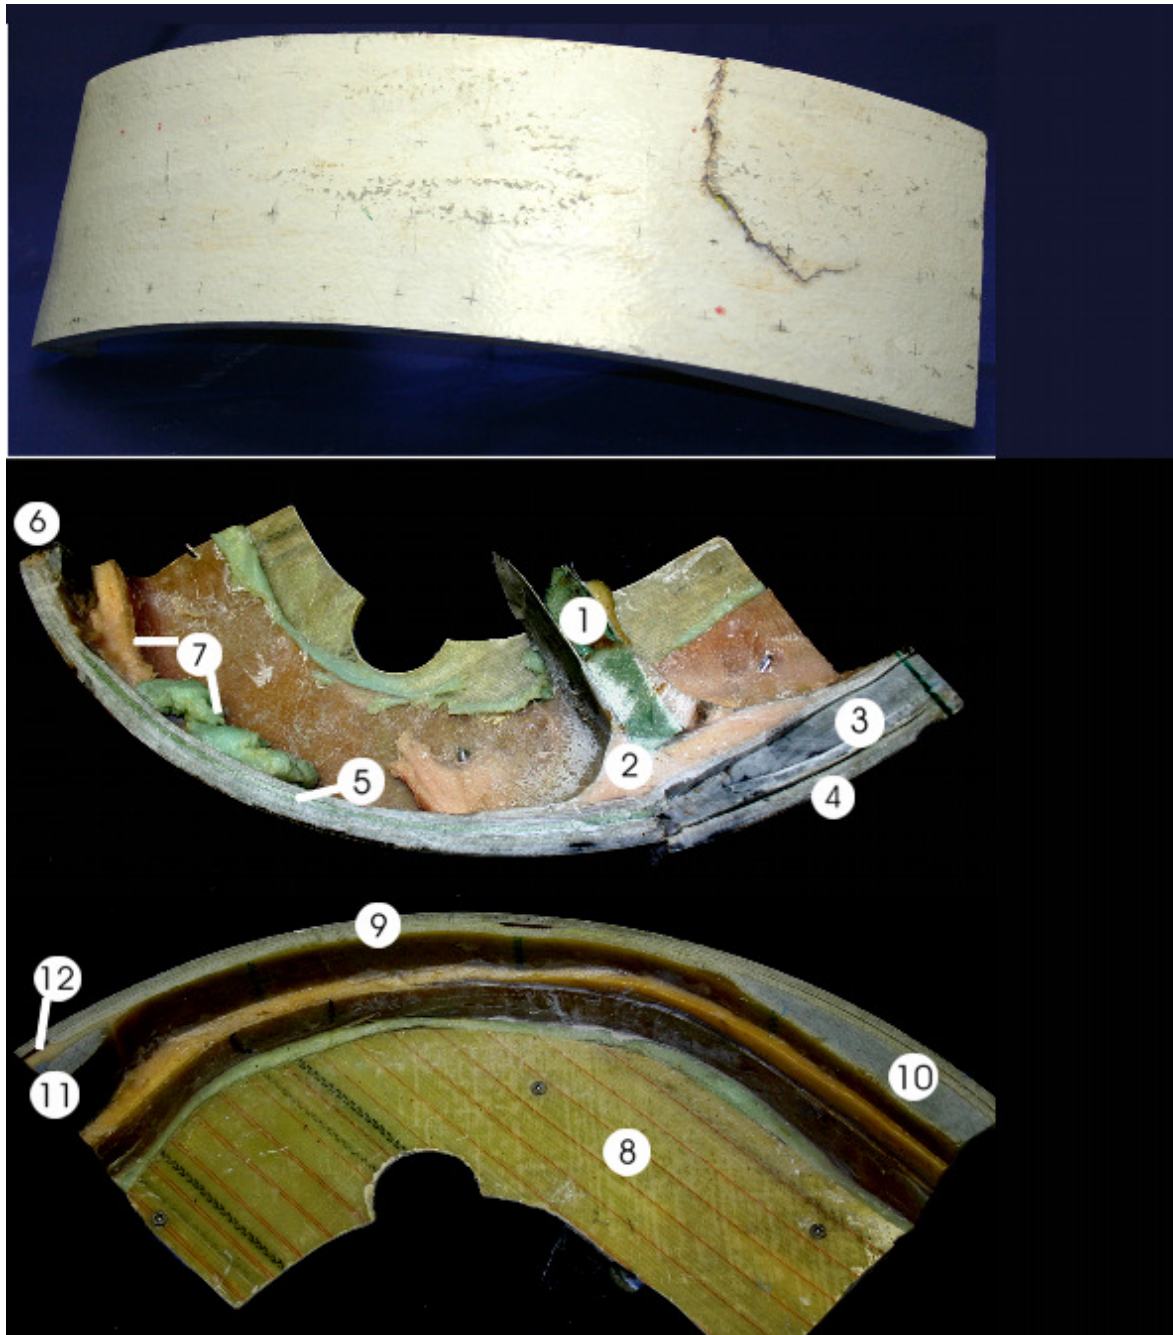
Aufsicht und Querschnitt der Rotorblattprobe.
